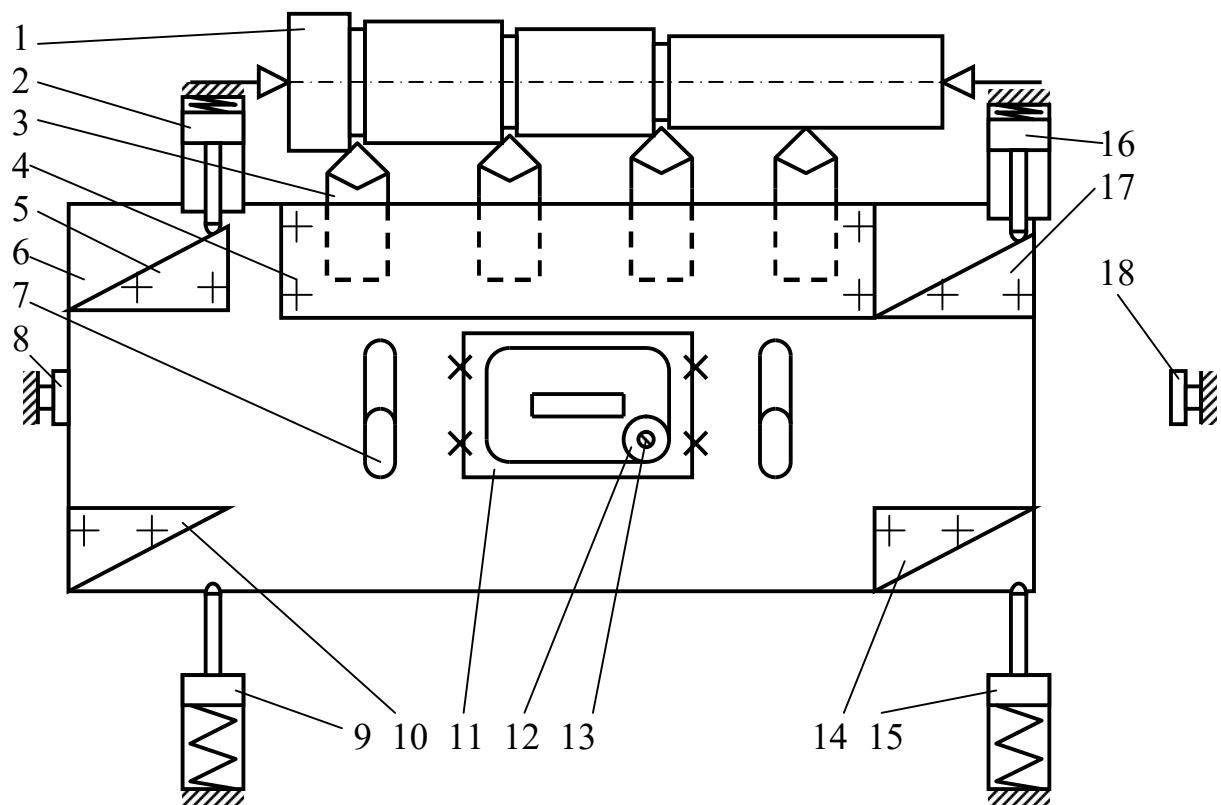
Схема налагодження різцетримача повздовжнього супорта одношпиндельного токарного багаторізцевого напівавтомата: 1 – еталон; 2, 9, 15, 16 – амортизатори; 3 – різці; 4 – притискна планка; 5, 10, 14, 17 – упори; 6 – різцетримач; 7 – кронштейни супорта; 8, 18 – шляхові перемикачі; 11 – копір; 12 – ролик; 13 – вісь
